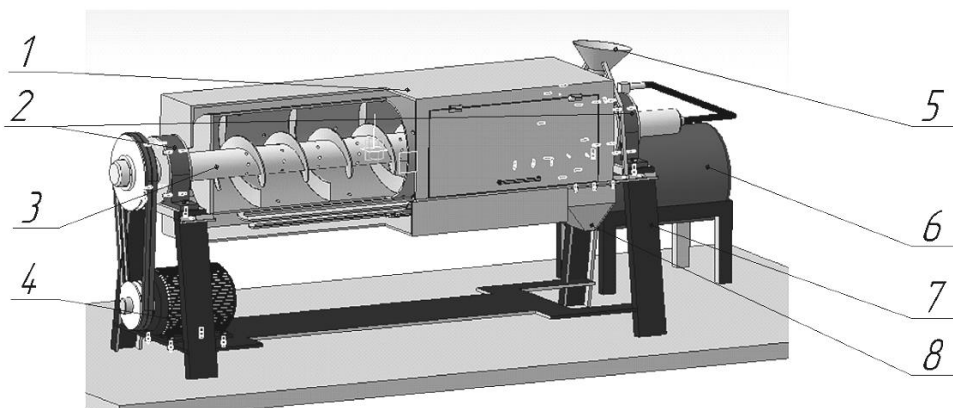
Загальний вигляд виготовлювача карамельного солоду: 1 – зовнішній кожух; 2 – підшипники; 3 – порожнистий вал шнека; 4 – електродвигун; 5 – завантажувальна горловина; 6 – генератор пари; 7 – корпус; 8 – вивантажувальна горловина.
